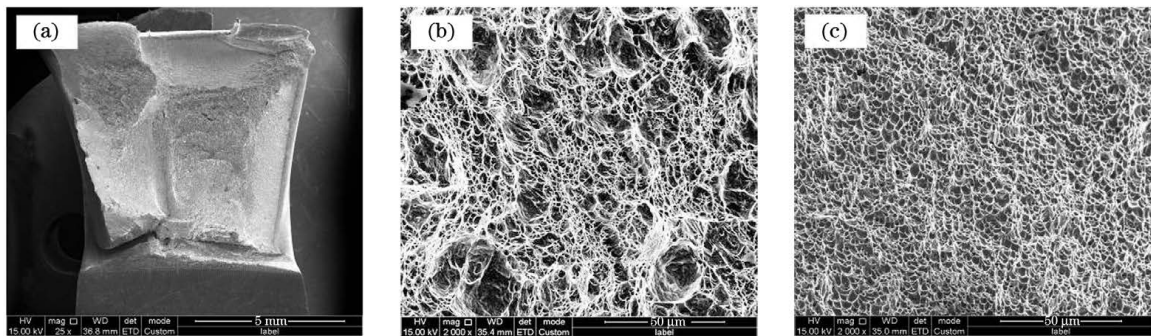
焊接速度为 1.2 m/min 时焊缝的冲击断口形貌。(a)宏观断口;(b)(c)韧窝
